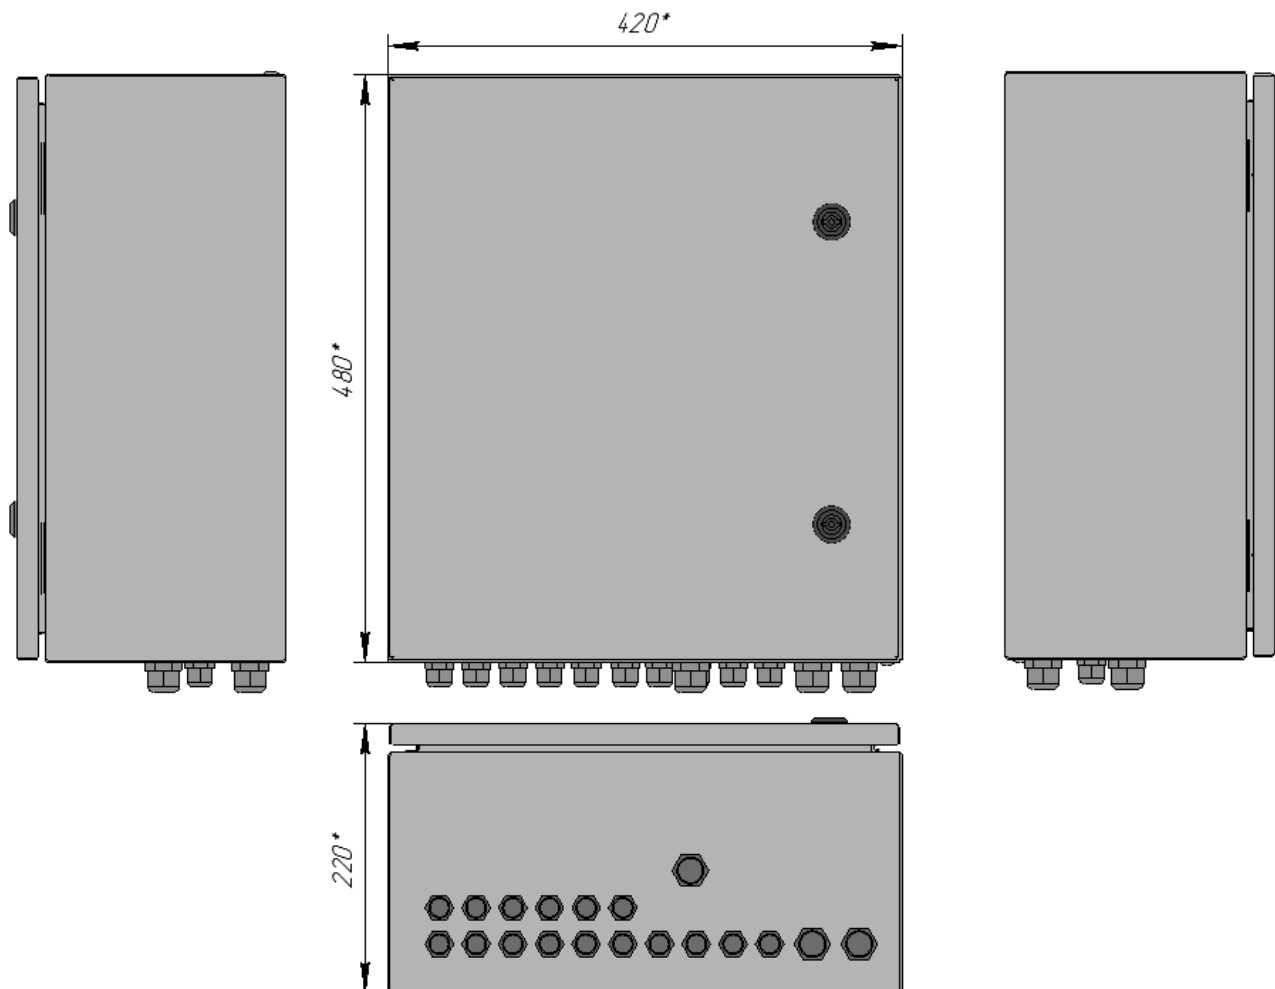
Внешний вид и габаритные размеры Узла доступа 172S2-F
